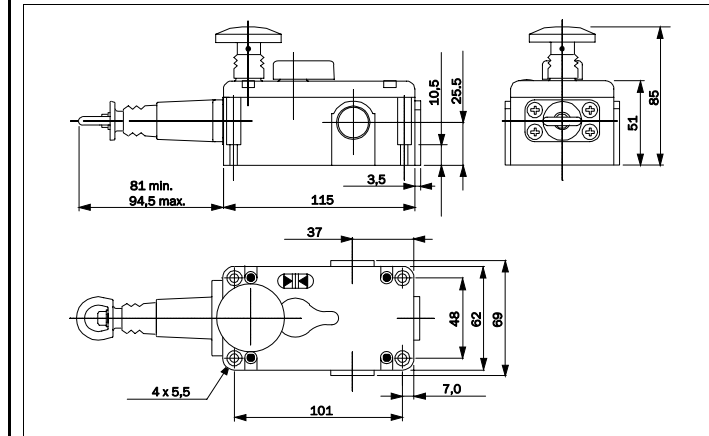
Croquis de dimensiones interruptores de cable i150-RP223 y i150-RP313 (mm)
